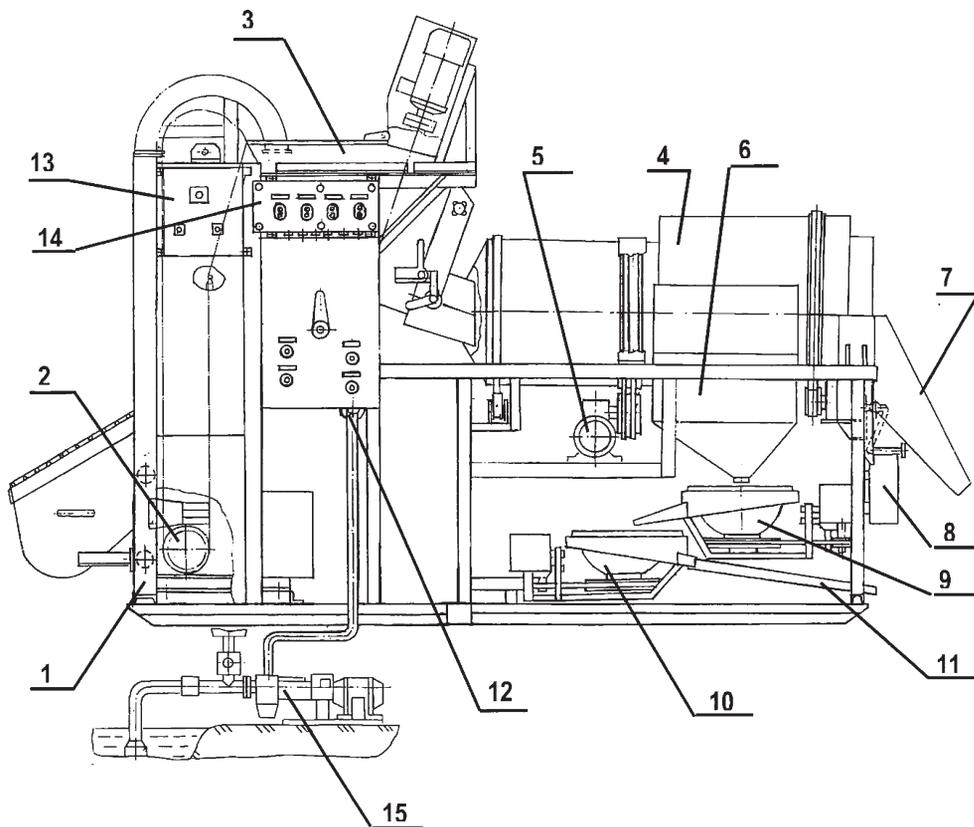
Установка обогатительная передвижная ПОУ4–3М: 1 — рама; 2 — механизм подъема; 3 — импеллерный дезинтегратор; 4 — барабан-грохот; 5 — привод барабана-грохота; 6 — сборник; 7 — блок лотков (шлюз); 8 — шлюз эфельный; 9 — сепаратор центробежный (основной); 10 — сепаратор центробежный (контрольный); 11 — лоток; 12 — система водораспределения; 13 — станция магнитная; 14 — пульт управления; 15 — станция насосная (в основной комплект не входит)
